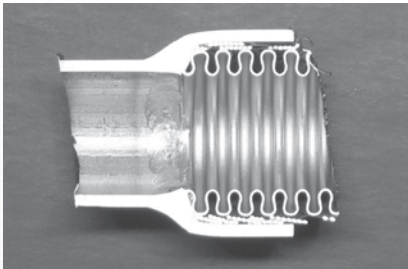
Schweißanbindung von HYDRA Schlauchleitungen
